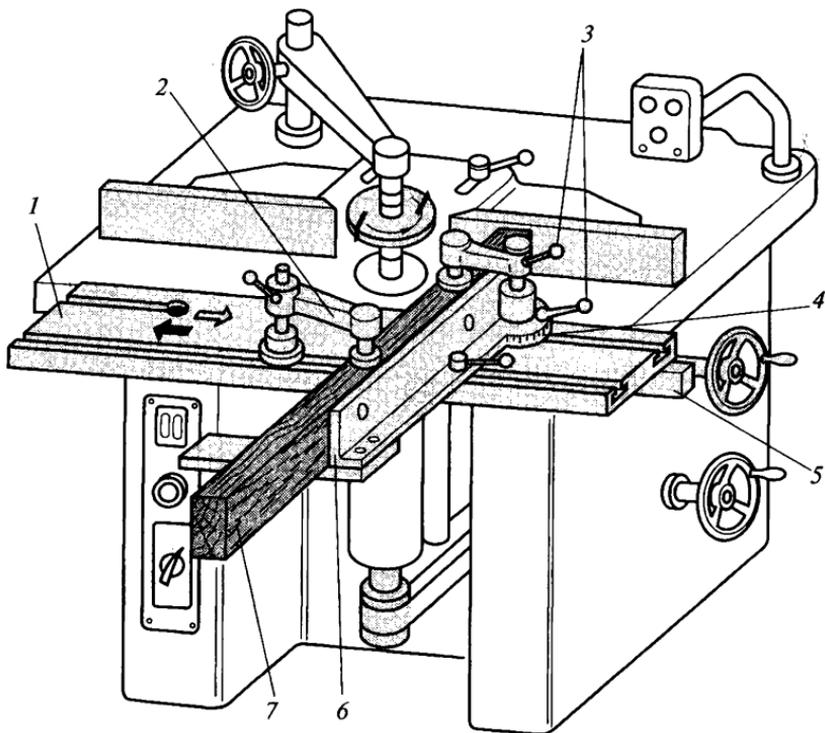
Фрезерный станок с шипорезной кареткой:
